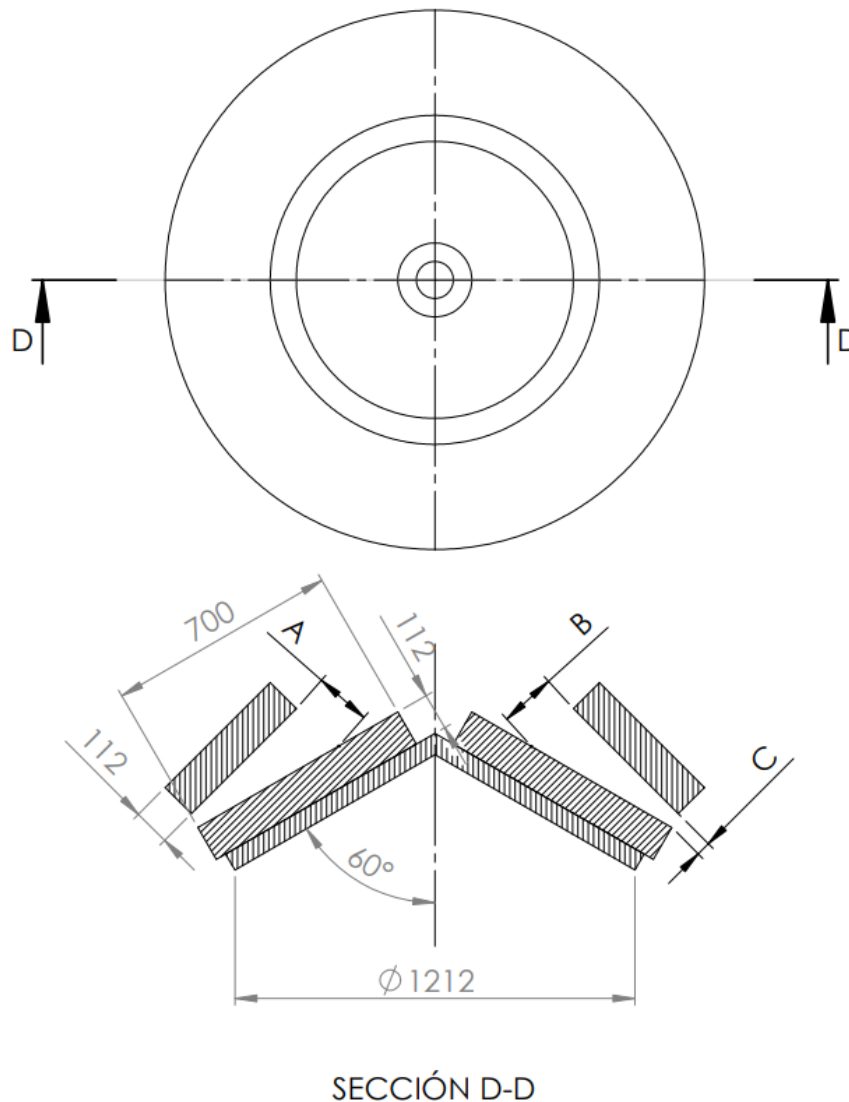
Plano del ensamblaje simplificado para cálculos teóricos
